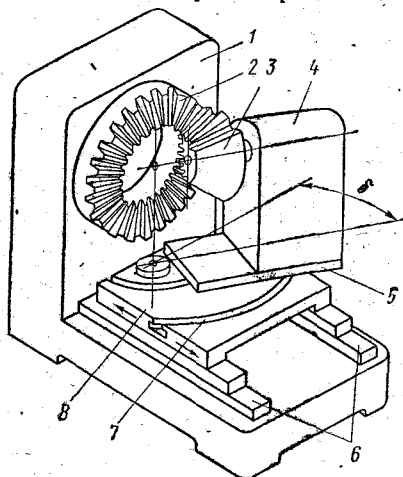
Схема компоновки зуборезного станка для нарезания конических зубчатых колес методом обкатки
